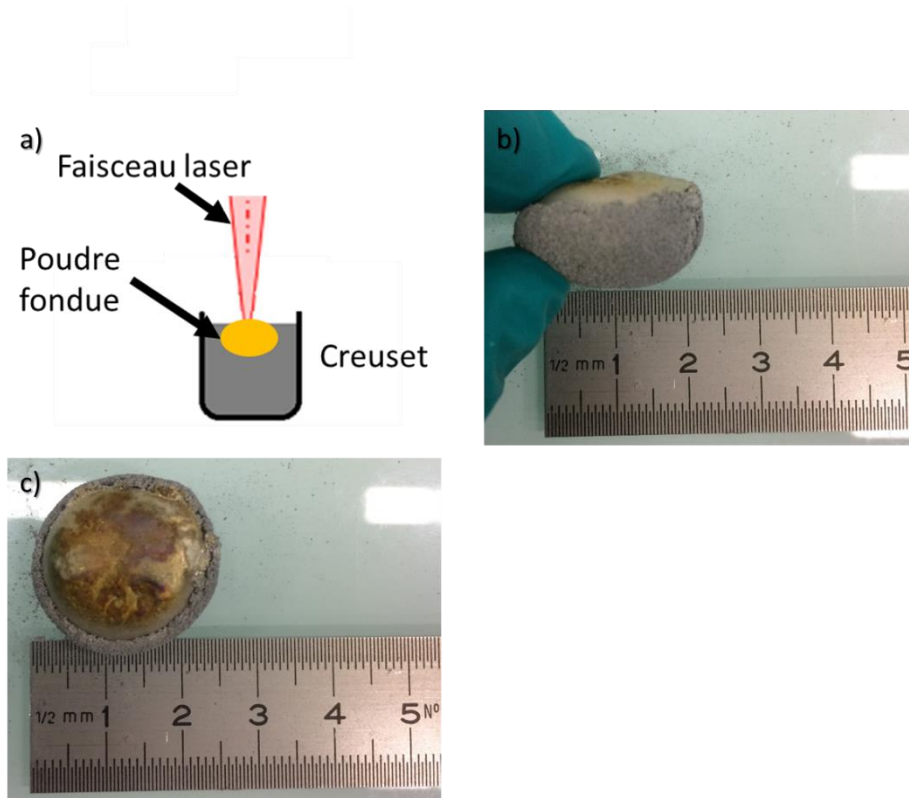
a) Schéma du procédé de fusion laser par creuset, b) Echantillon fabriqué par fusion en creuset vue de côté et c) vue de dessus
